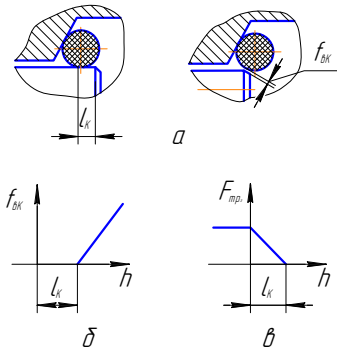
Елементи розрахункової схеми зворотно-запобіжного контуру з зворотно-запобіжним клапаном:
